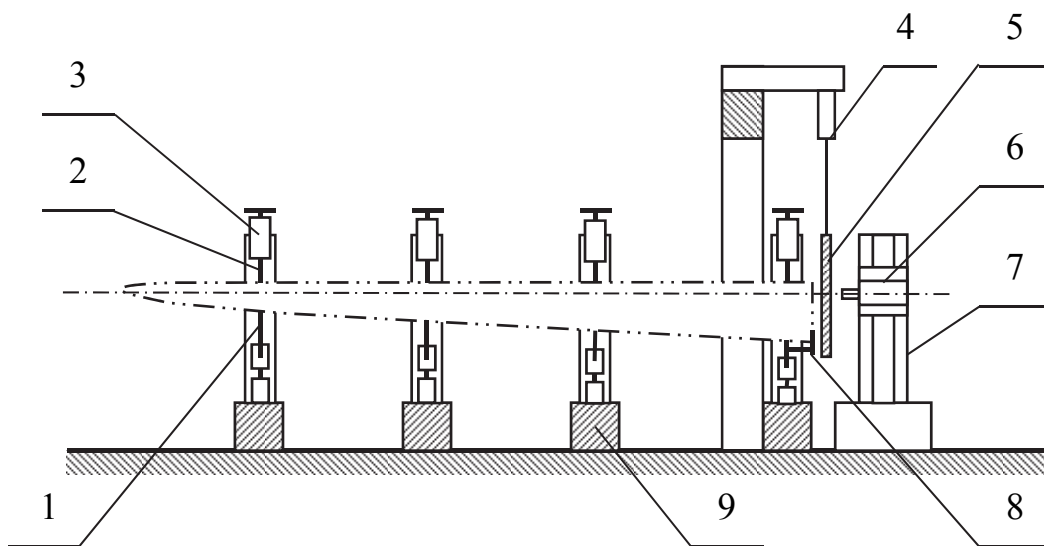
Принципиальная схема разделочного станда для обработки стыка крыла: 1 – ложемент; 2 – рубильник; 3 – прижимной механизм; 4 – механизм подъема; 5 – ПРС; 6 – разделочный агрегат; 7 – стойка; 8 – упор; 9 – балка
